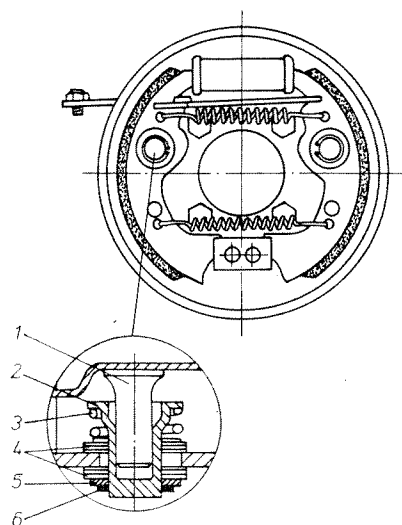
Freno de tambor con dispositivo autorregulable.
